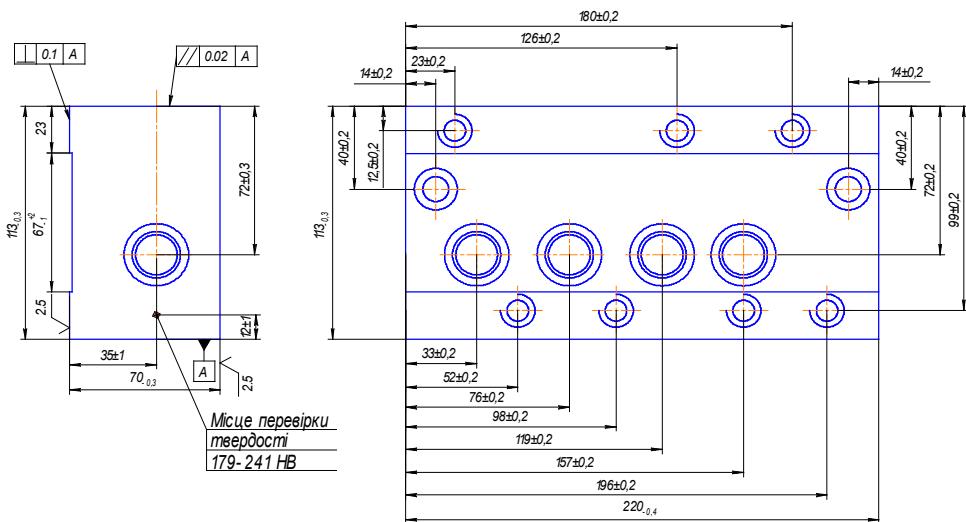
«Корпус гідророзподільника» виробництва ВАТ «Львівський завод фрезерних верстатів»
